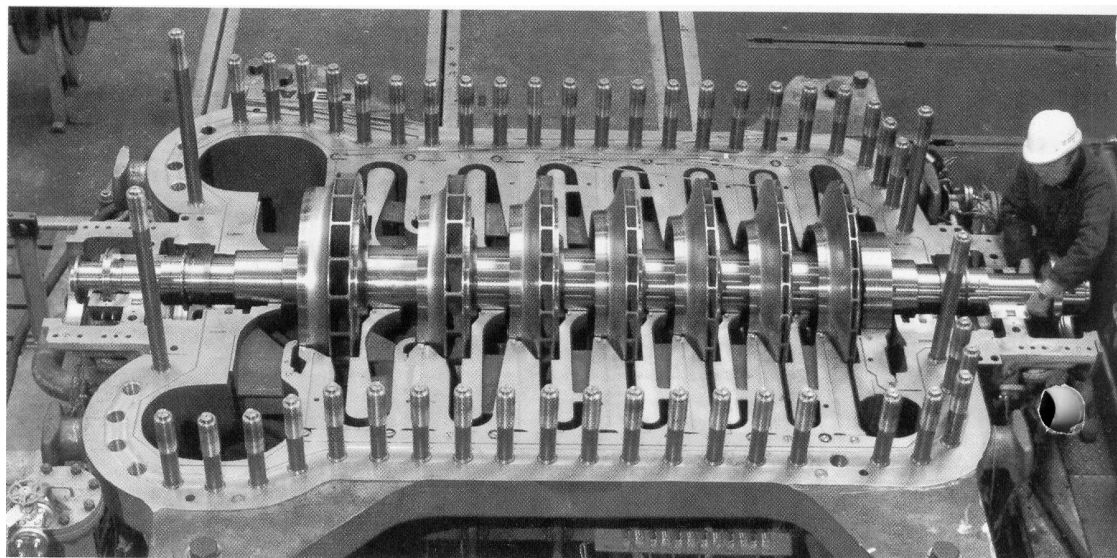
Семиступенчатый одновальный центробежный компрессор для одного из химических производств (верхняя часть корпуса снята)
